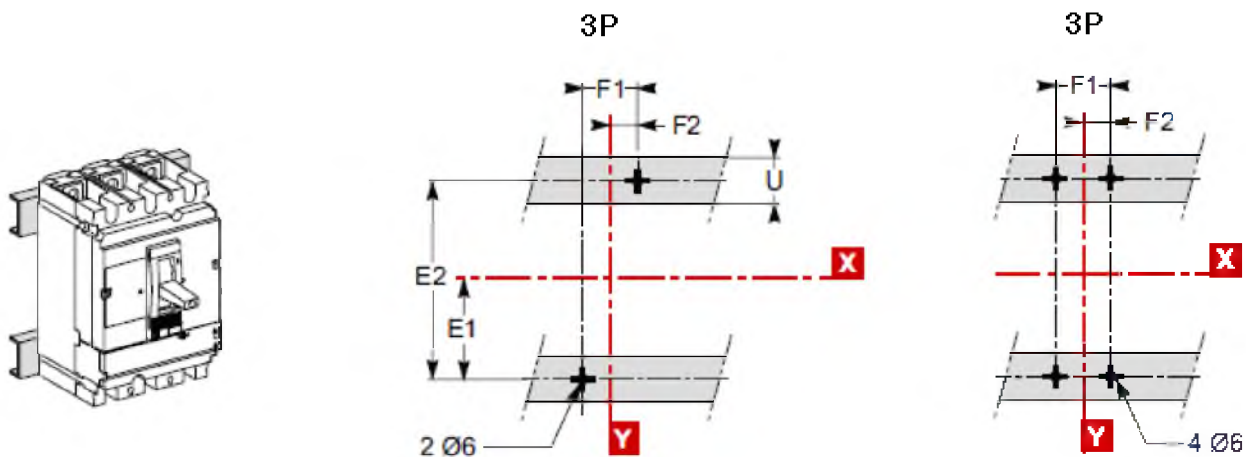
Установочные размеры ВА-СЭЦ-МС100/160/250/400/630 на профиле
